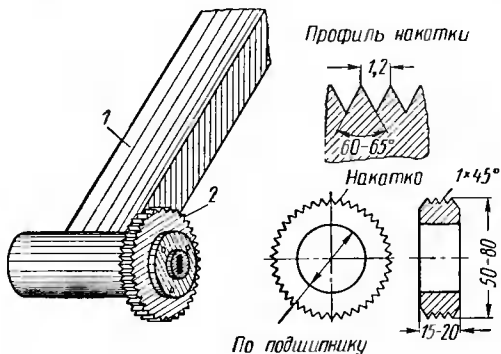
Накатка для подготовки цилиндрических поверхностей:
